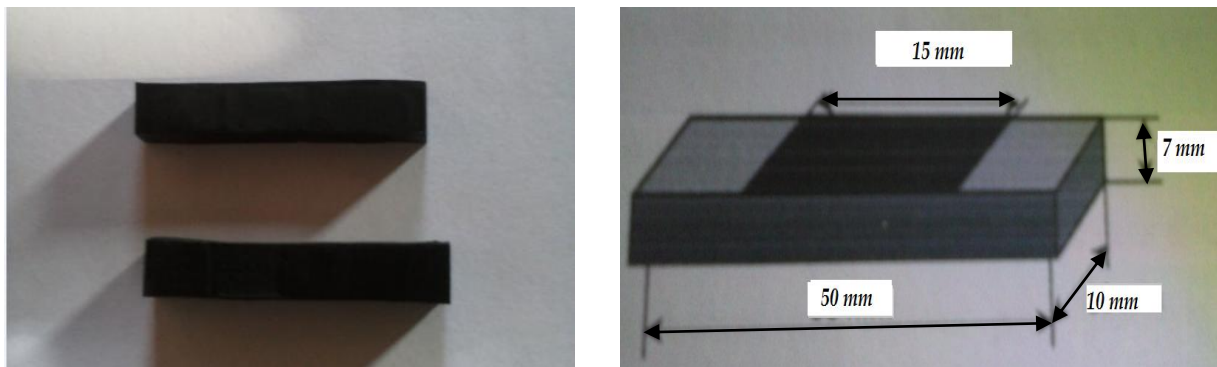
photographie et dimensionnement des échantillons pour l'usure abrasive
